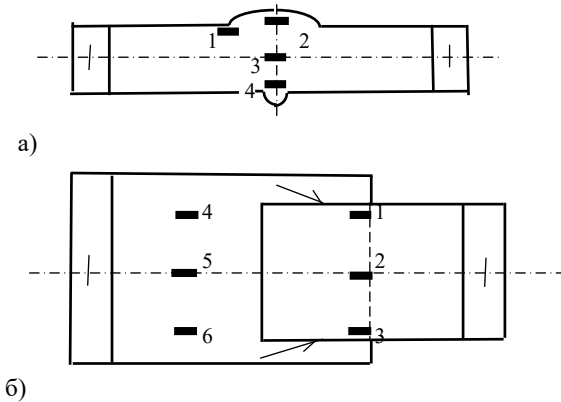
Модели сварных стыковых (а) и нахлесточных (б) соединений;
